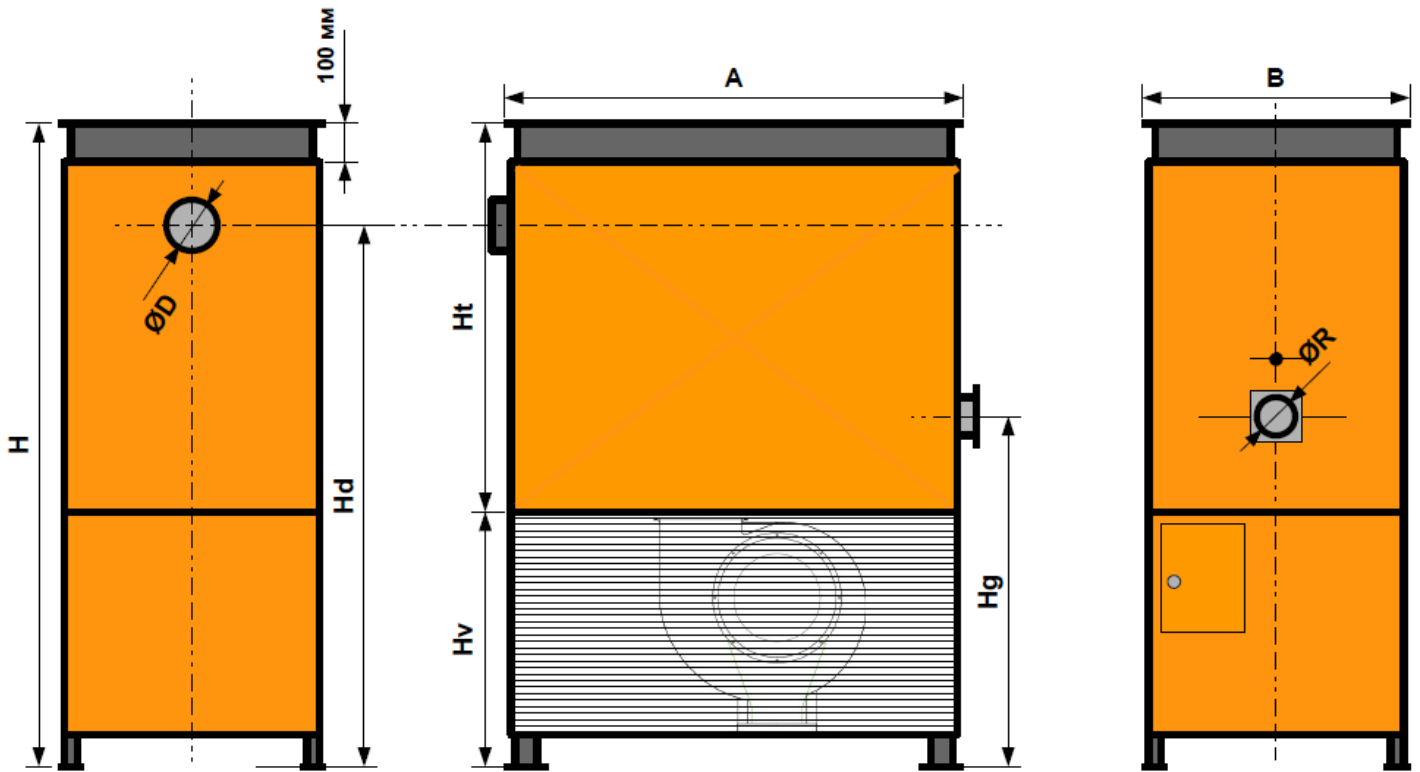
Габаритные размеры воздухонагревателей (теплообменников) серий VT-K
